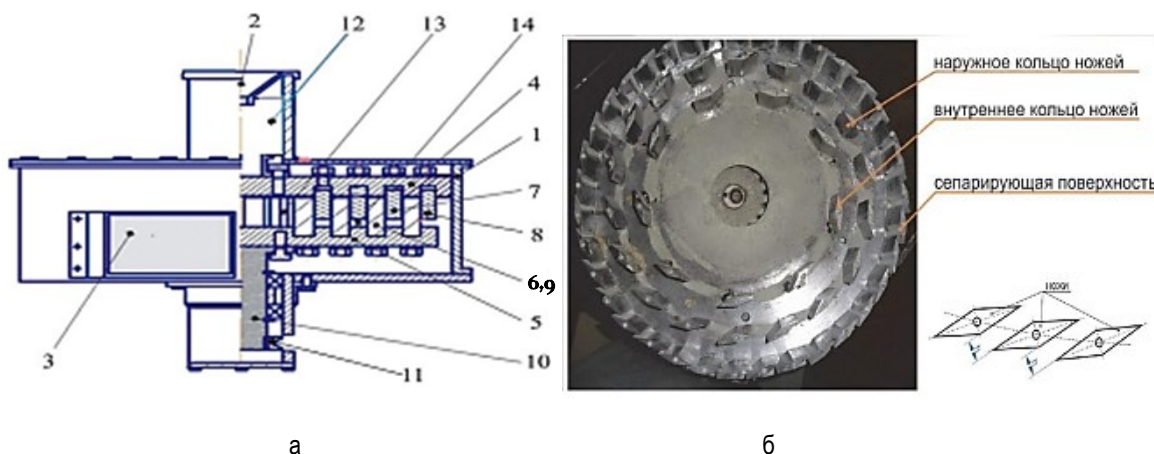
Схема центробежно-роторного дробильного аппарата:
